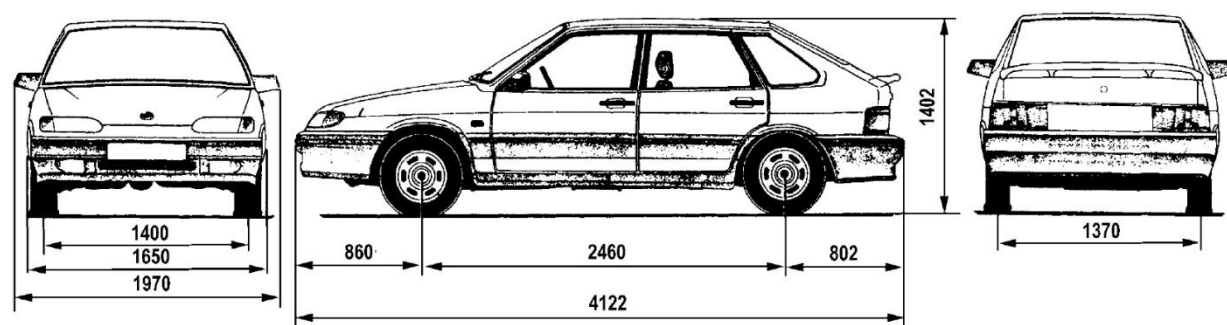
Внешний вид автомобиля ВАЗ-2114
